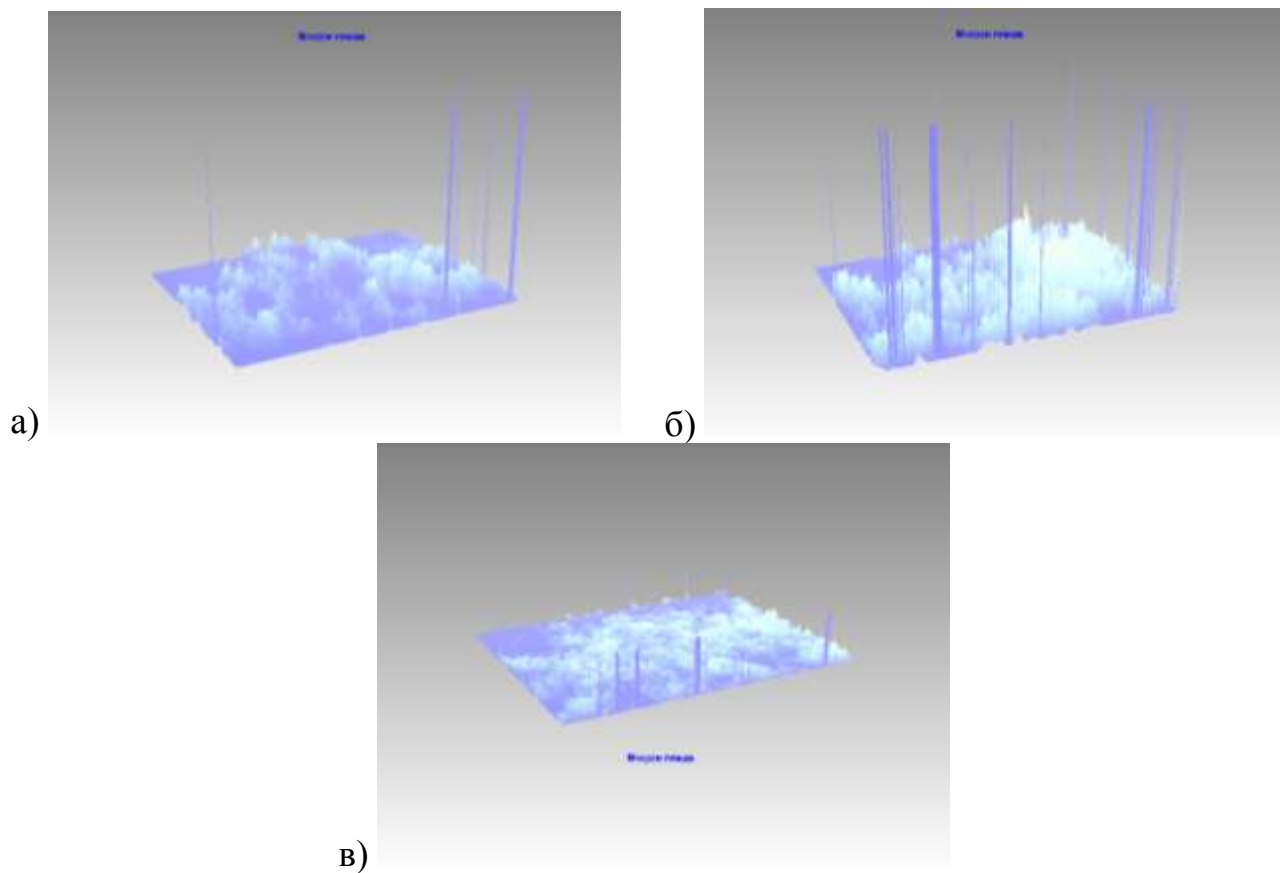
3D модель структури металла сварного соединения в кольцевом образце: а) сварка ТВЧ; б) дуговая сварка без вибрации; в) дуговая сварка с вибрацией
